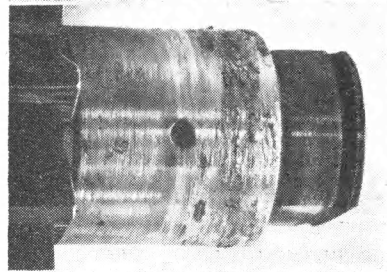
Поверхность трения валика регулятора оборотов авиадвигателя, подвергшаяся износу в условиях схватывания 1-го рода.
